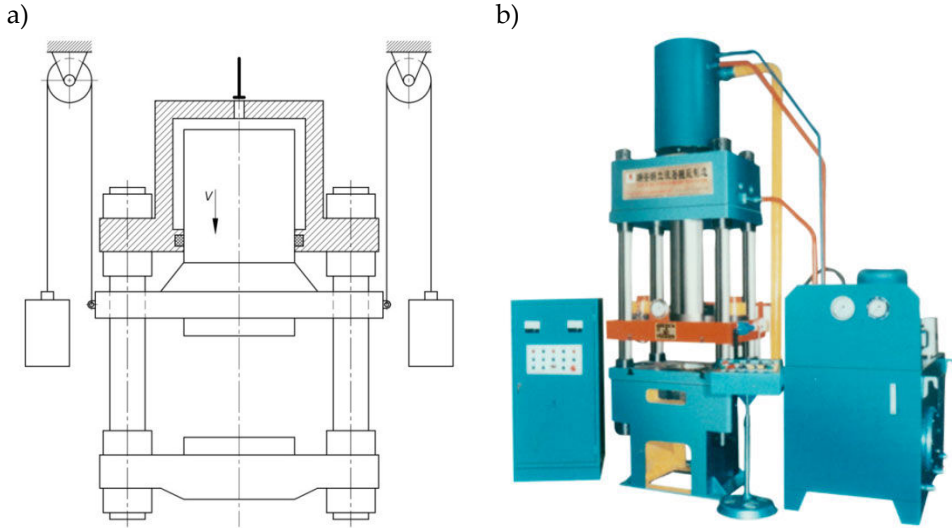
Prasa z napędem hydraulicznym dolno cylindrowa: a) schemat i zasada działania, b) przykładowa konstrukcja prasy o nacisku 2500 kN [56]
